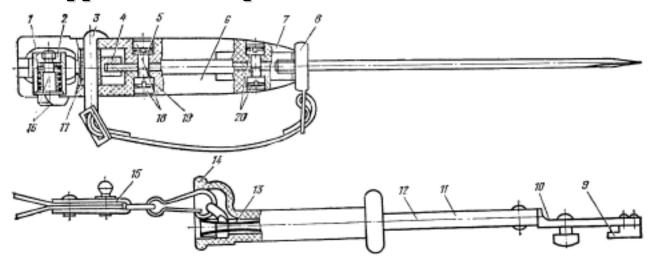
Нож–штык 6X3: 1 — пружина защелки; 2 — основание защелки; 3 — ремень в сборе ; 4 — наконечник; 5 — винт; 6 — правая щечка; 7 — левая щечка; 8 — кольцо; 9 — упор; 10 — резак; 11 — ножна; 12 — ножна в сборе; 13 — фиксатор; 14 — резиновый предохранитель; 15 — подвеска собранная; 16 — винт защелки ножа с кнопкой; 17 — трубка; 18 — пробка; 19 — гайка; 20 — пробка
